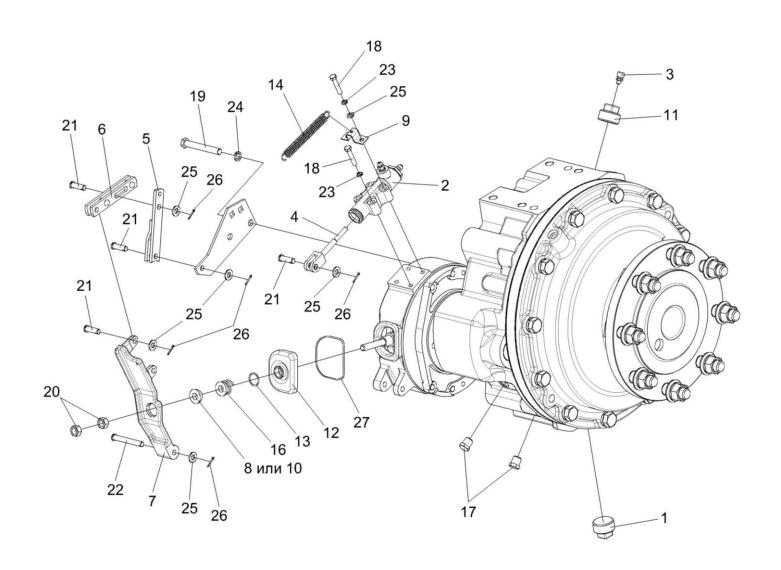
Редуктор бортовой правый УЭС 0107070А-03
